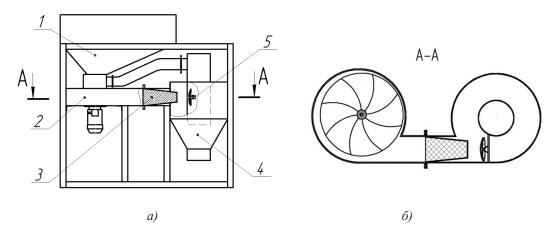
Пневмомеханическое устройство для обрушивания семян подсолнечника: а) — общий вид устройства; б) — разрез A-A; 1 —бункер питающий; 2 — вентилятор; 3 — сетчатый рабочий орган; 4 — осадитель; 5 — сферическая рабочая пластина
